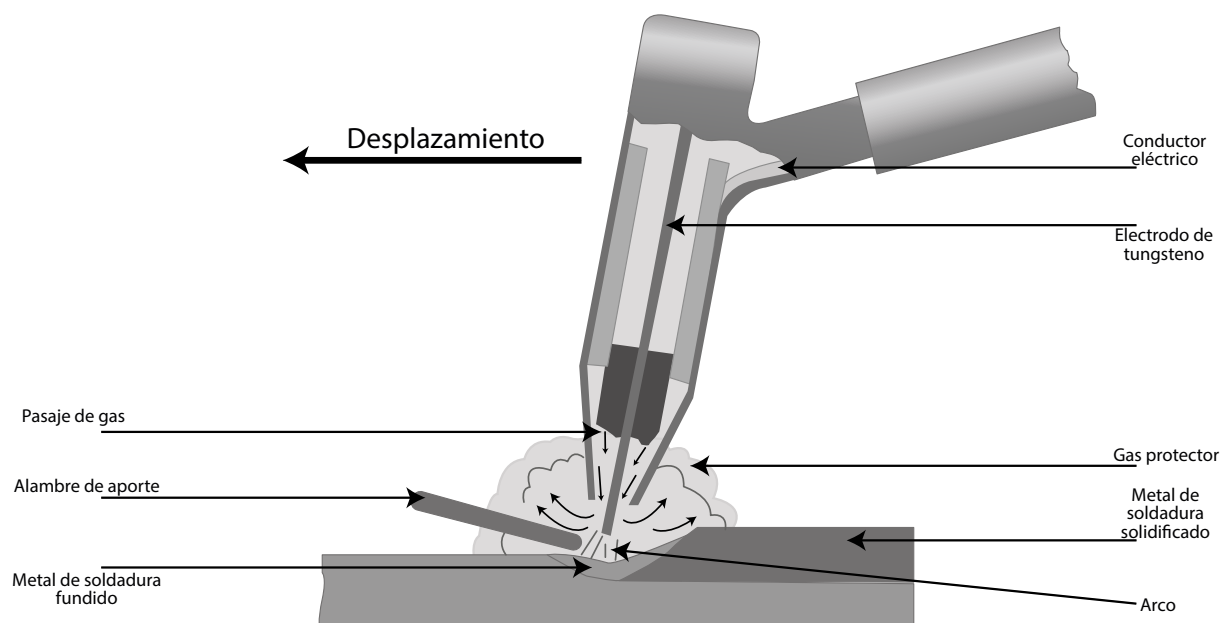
Soldadura por arco de tungsteno y gas
